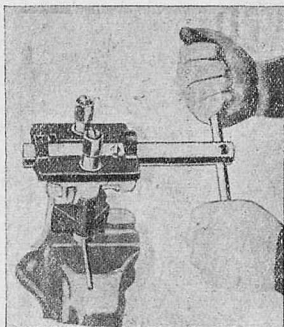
Процесс нарезки смазочных канавок крышки коренного подшипника
